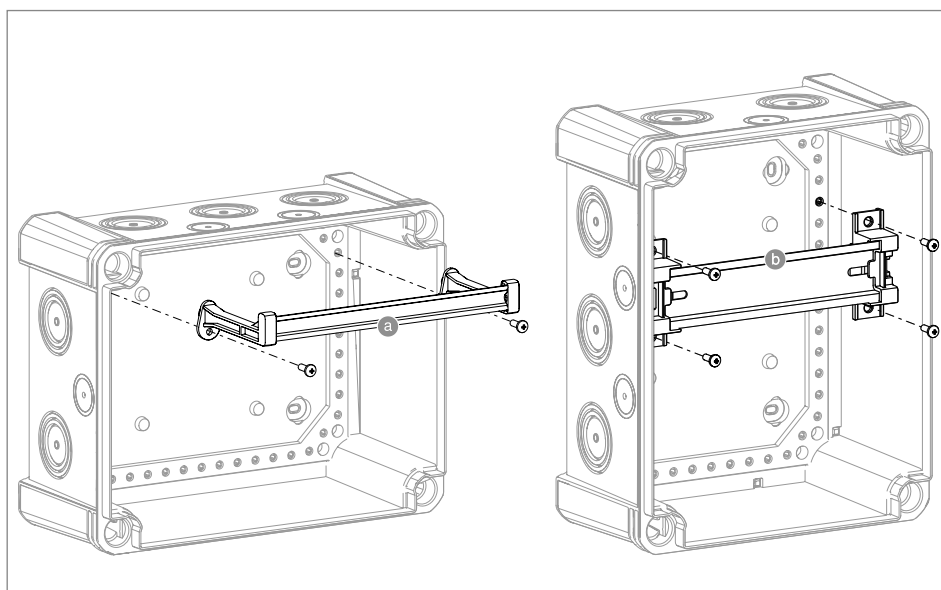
Montage du rail DIN profilé de type 46277 et type 2069 dans la boîte de dérivation
